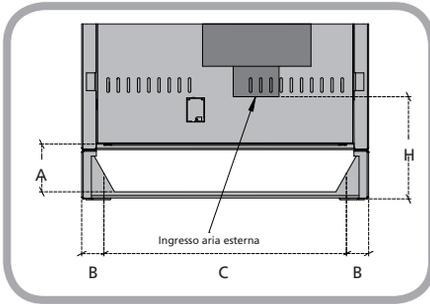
Modi di collegamento della presa d'aria della cucina a legna
